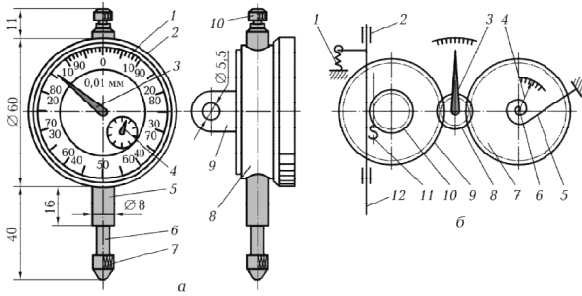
Індикаторна вимірювальна головка (індикатор годинного типу): а – загальний вигляд: 1 – вимірювальна шкала; 2 – кільце для встановлення шкали на нуль; 3 – стрілка-показчик; 4 – стрілка відліку числа оборотів; 5 – гільза; 6 – стрижень; 7 – наконечник; 8 – корпус; 9 – кріпильне вушко; 10 – головка відведення вимірювального стрижня; б – кінематична схема: 1, 5 – пружини; 2 – гільза; 3 – стрілка-показчик; 4 – стрілка контролю числа оборотів; 6 – вісь; 7-10 – зубчасті колеса; 11 – зубчаста рейка; 12 – наконечник
